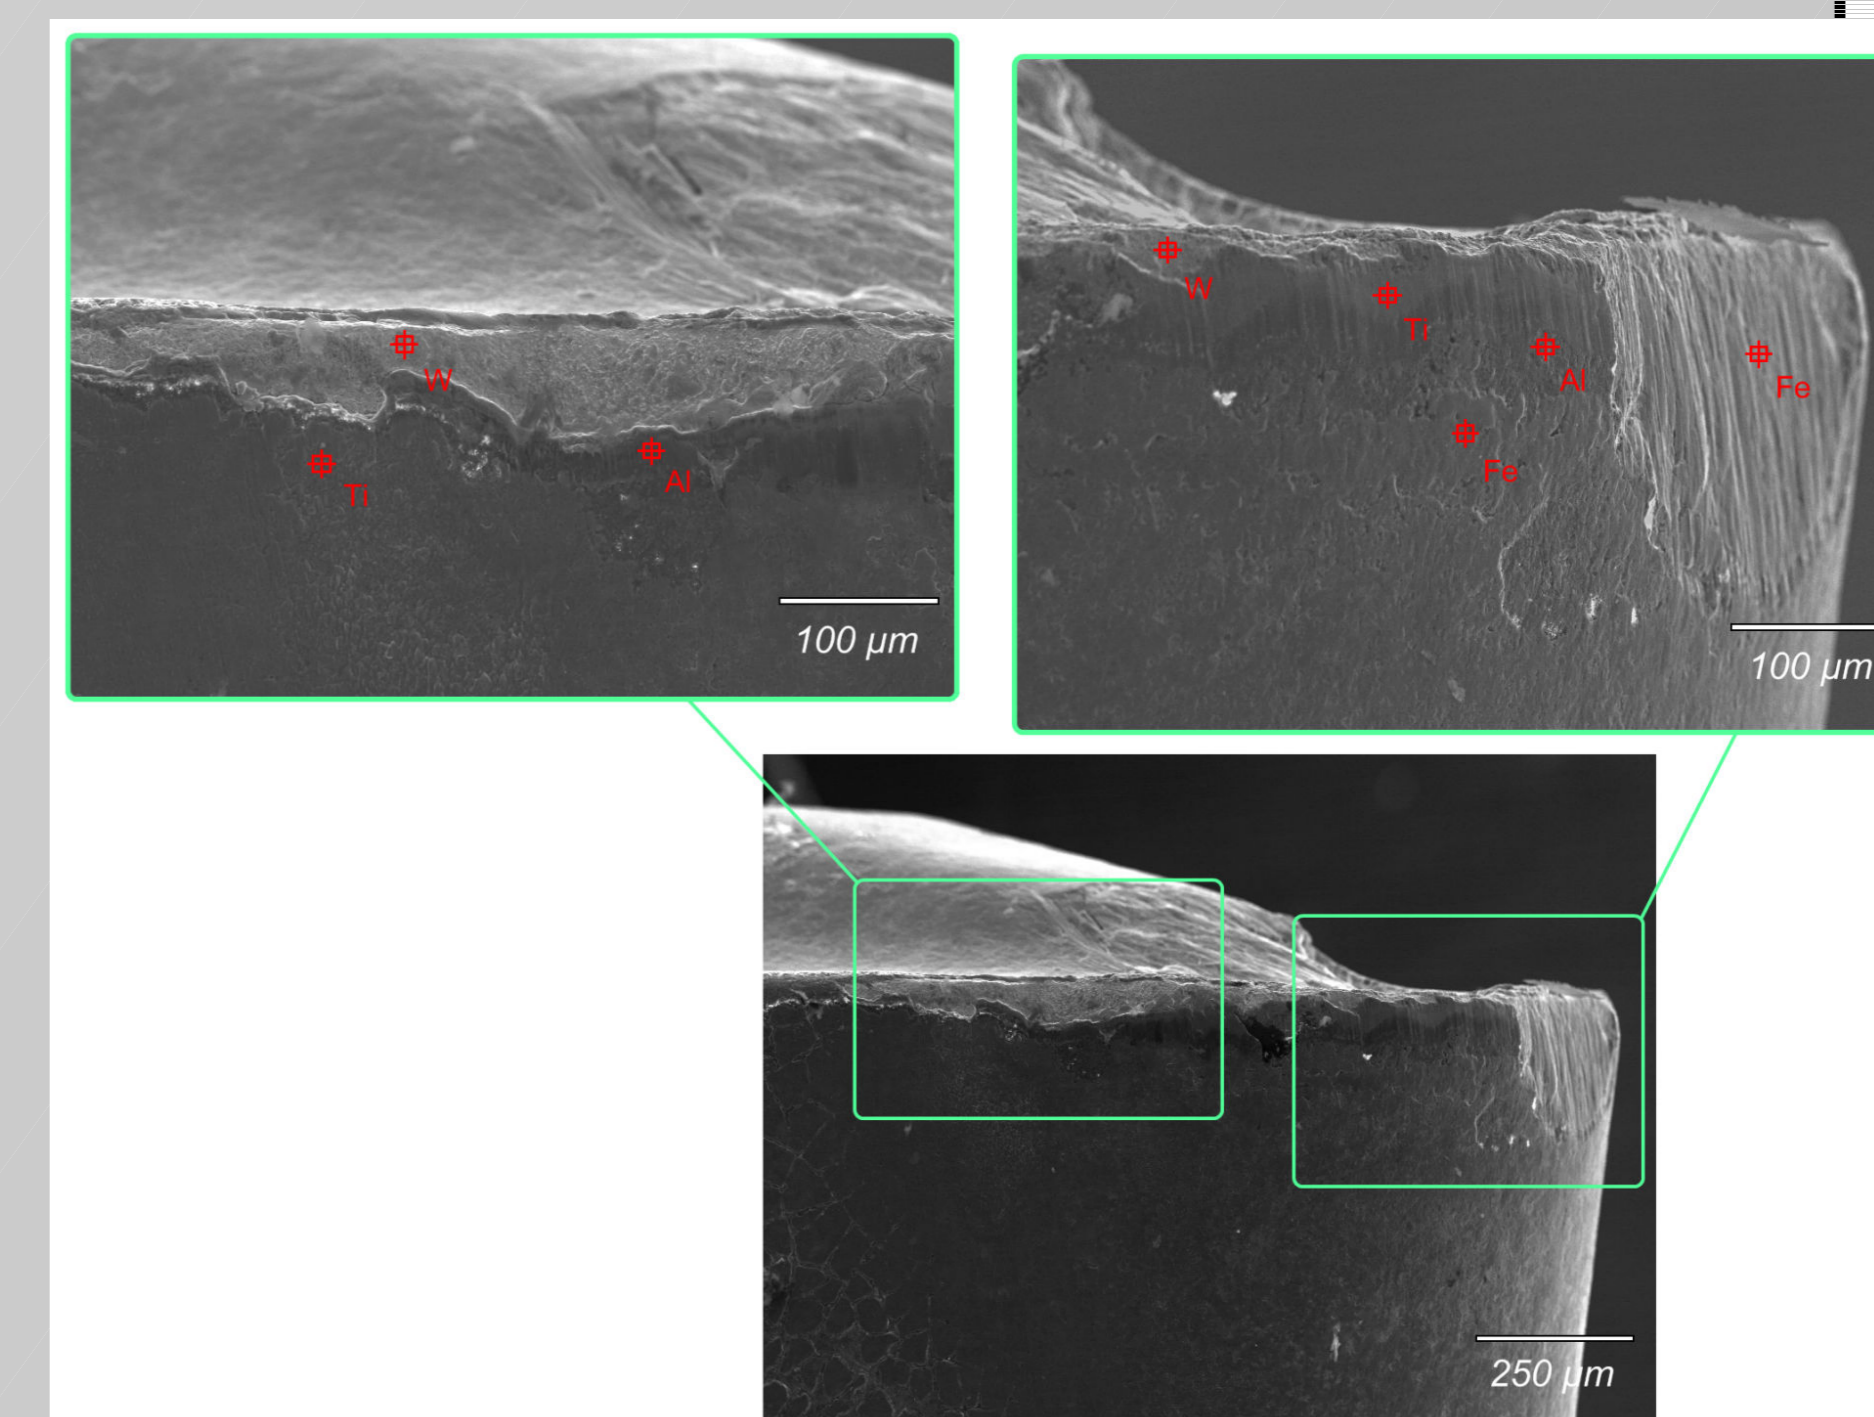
Imagem da superfície de folga da ferramenta P15 e fluido de corte sob alta pressão.
